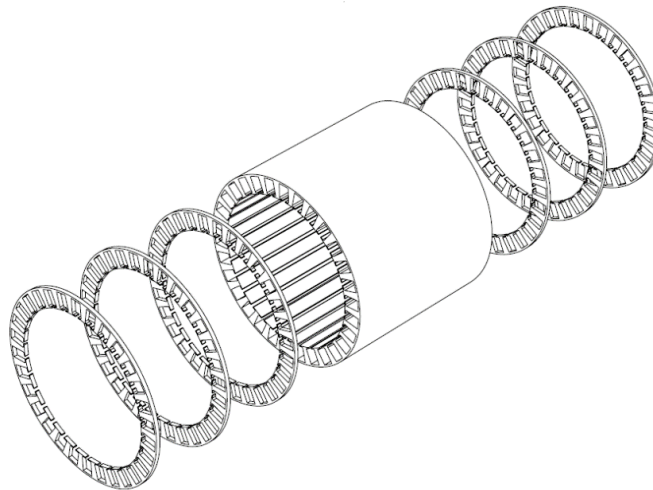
Explosionado estátor de polos lisos de una máquina eléctrica
